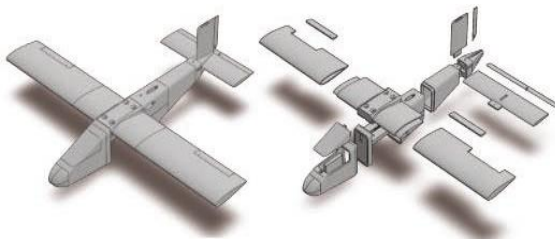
Vistas em perspetiva da configuração base unida e em exploded view (CAD)
